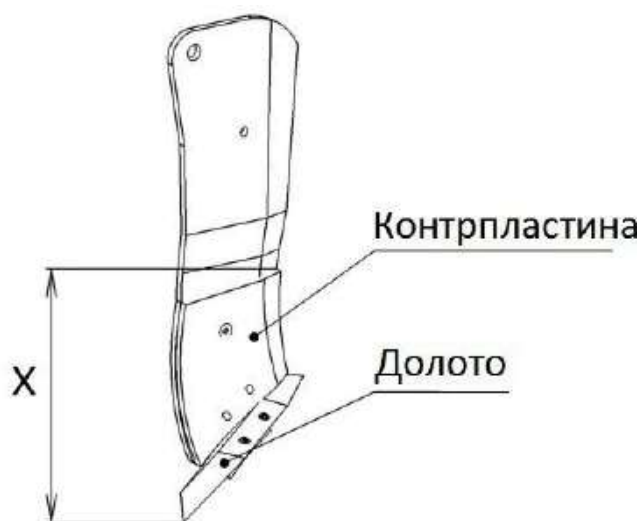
Регулировка глубина работы вогнутых зубьев
